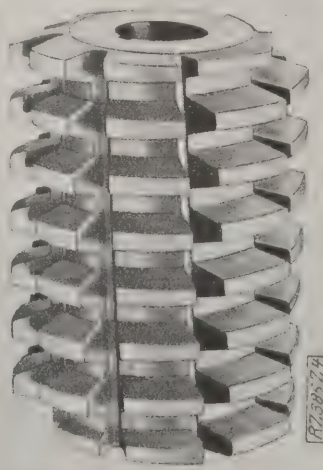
Üblicher Schraubenfräser für Stirnräderherzeugung.
